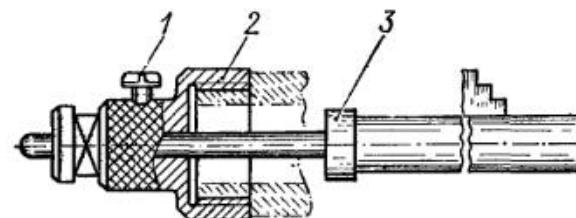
Упор для длинных заготовок, закрепляемых в патроне
